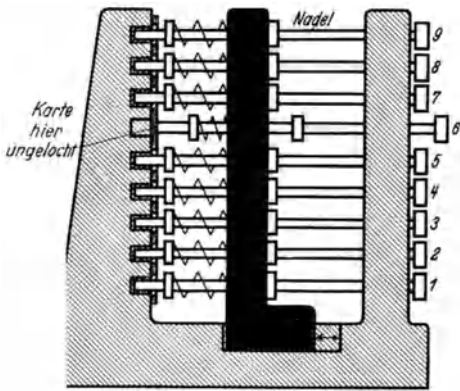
Zur Steuerung einer Bewegung in 9 verschiedenen Weglängen sind 9 Stoßkupplungen wie in Abb. 541 vereinigt. Für die zu steuernde Weglänge (6) hat die Karte kein Loch, für die übrigen 8 ungenutzten Stoßkupplungen 8 Löcher.
